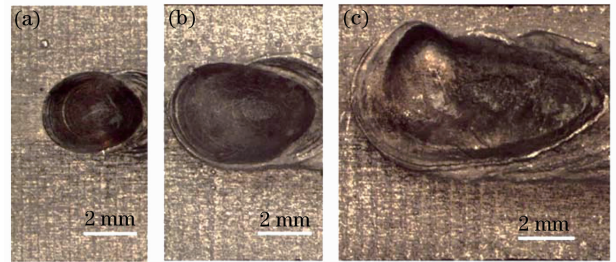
焊缝末端弧坑。(a)激光焊接;
